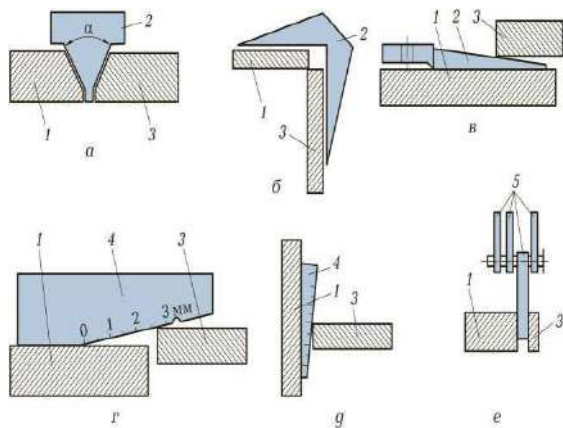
Контроль качества сборки деталей к сварке с использованием: а – шаблона для проверки угла а разделки кромок; б – шаблона для проверки прямого угла между кромками; в – шаблона для проверки зазора между кромками; г – измерительной линейки для определения превышения кромки; д – измерительной линейки для измерения зазора в тавровом соединении; е – шупа для определения зазора в стыковом соединении.
